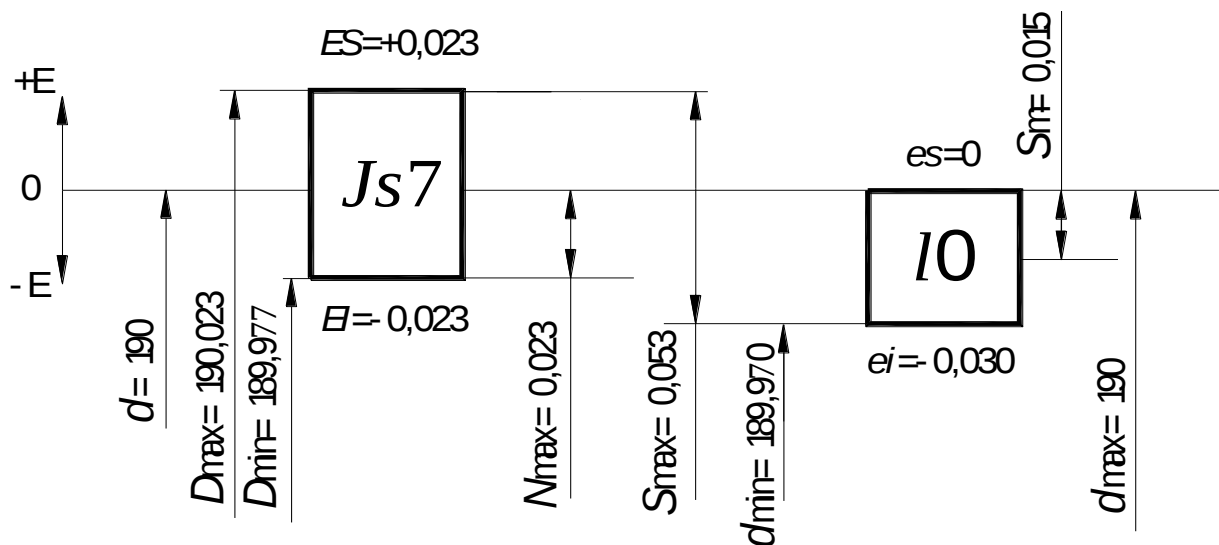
Схема расположения полей допусков наружного кольца подшипника и отверстия
